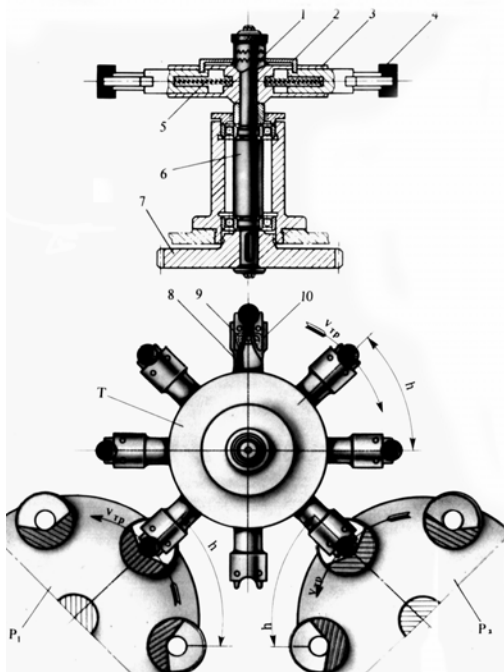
Транспортный ротор с клещевыми захватными органами:
